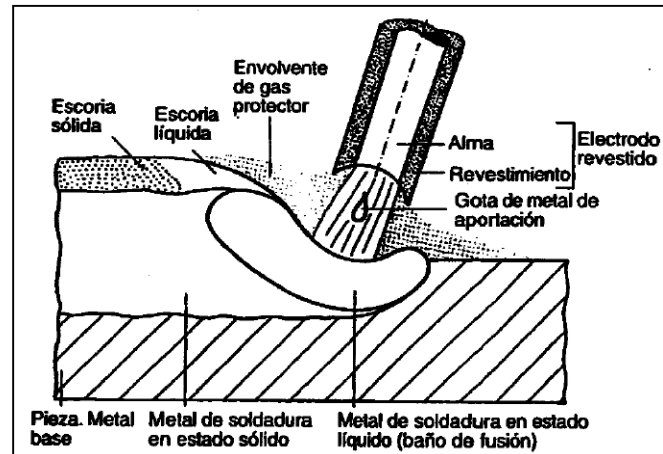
Esquema del Proceso de soldadura SMAW (1)
